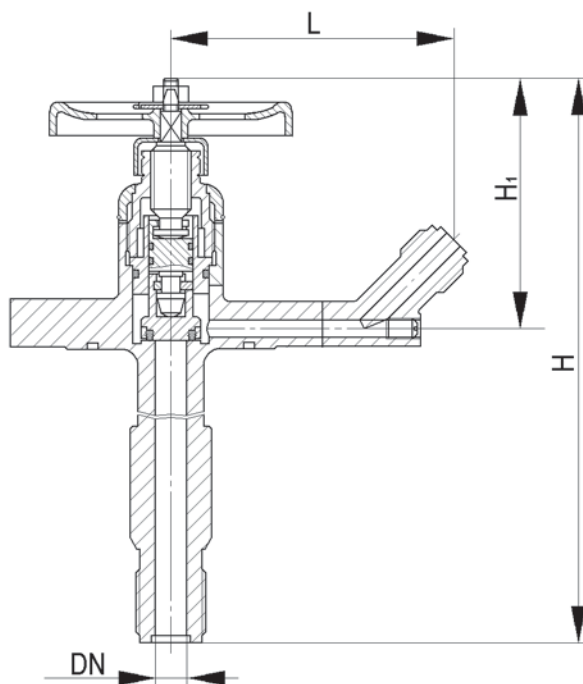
Клапан запорный угловой штуцерный
